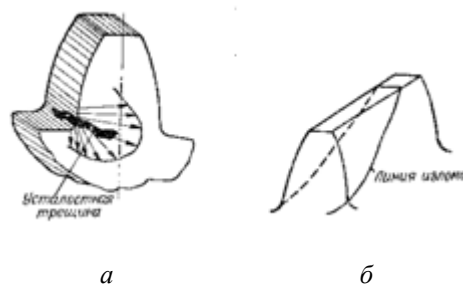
Виды разрушения зубьев : а - распространение изгибной усталостной трещины; б - излом зубьев косозубых и шевронных зубчатых колес
